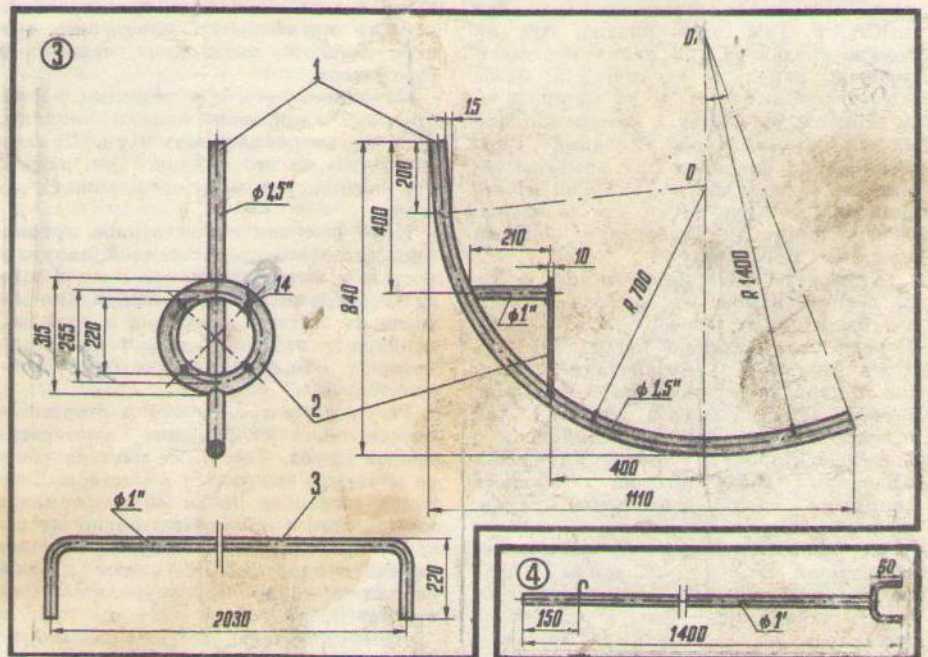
Основные детали опрокидывателя: 1 — дуга сектора; 2 — фланец; 3 — соединительная труба.
